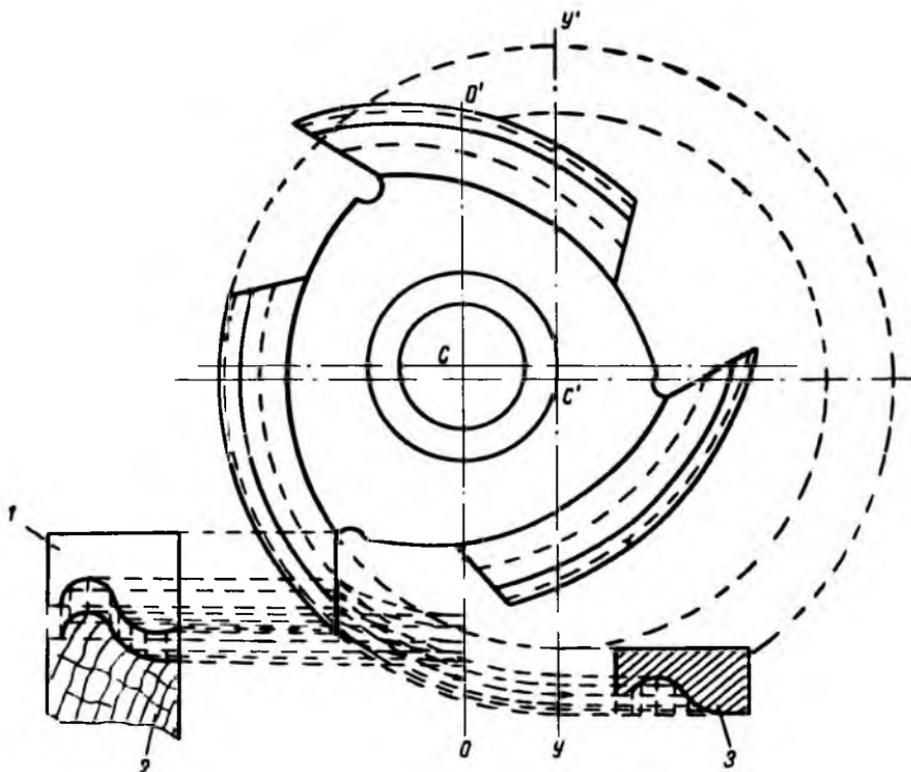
Графическое построение профиля поперечного сечения резца трех-резцовой фрезерной головки по профилю изделия:
